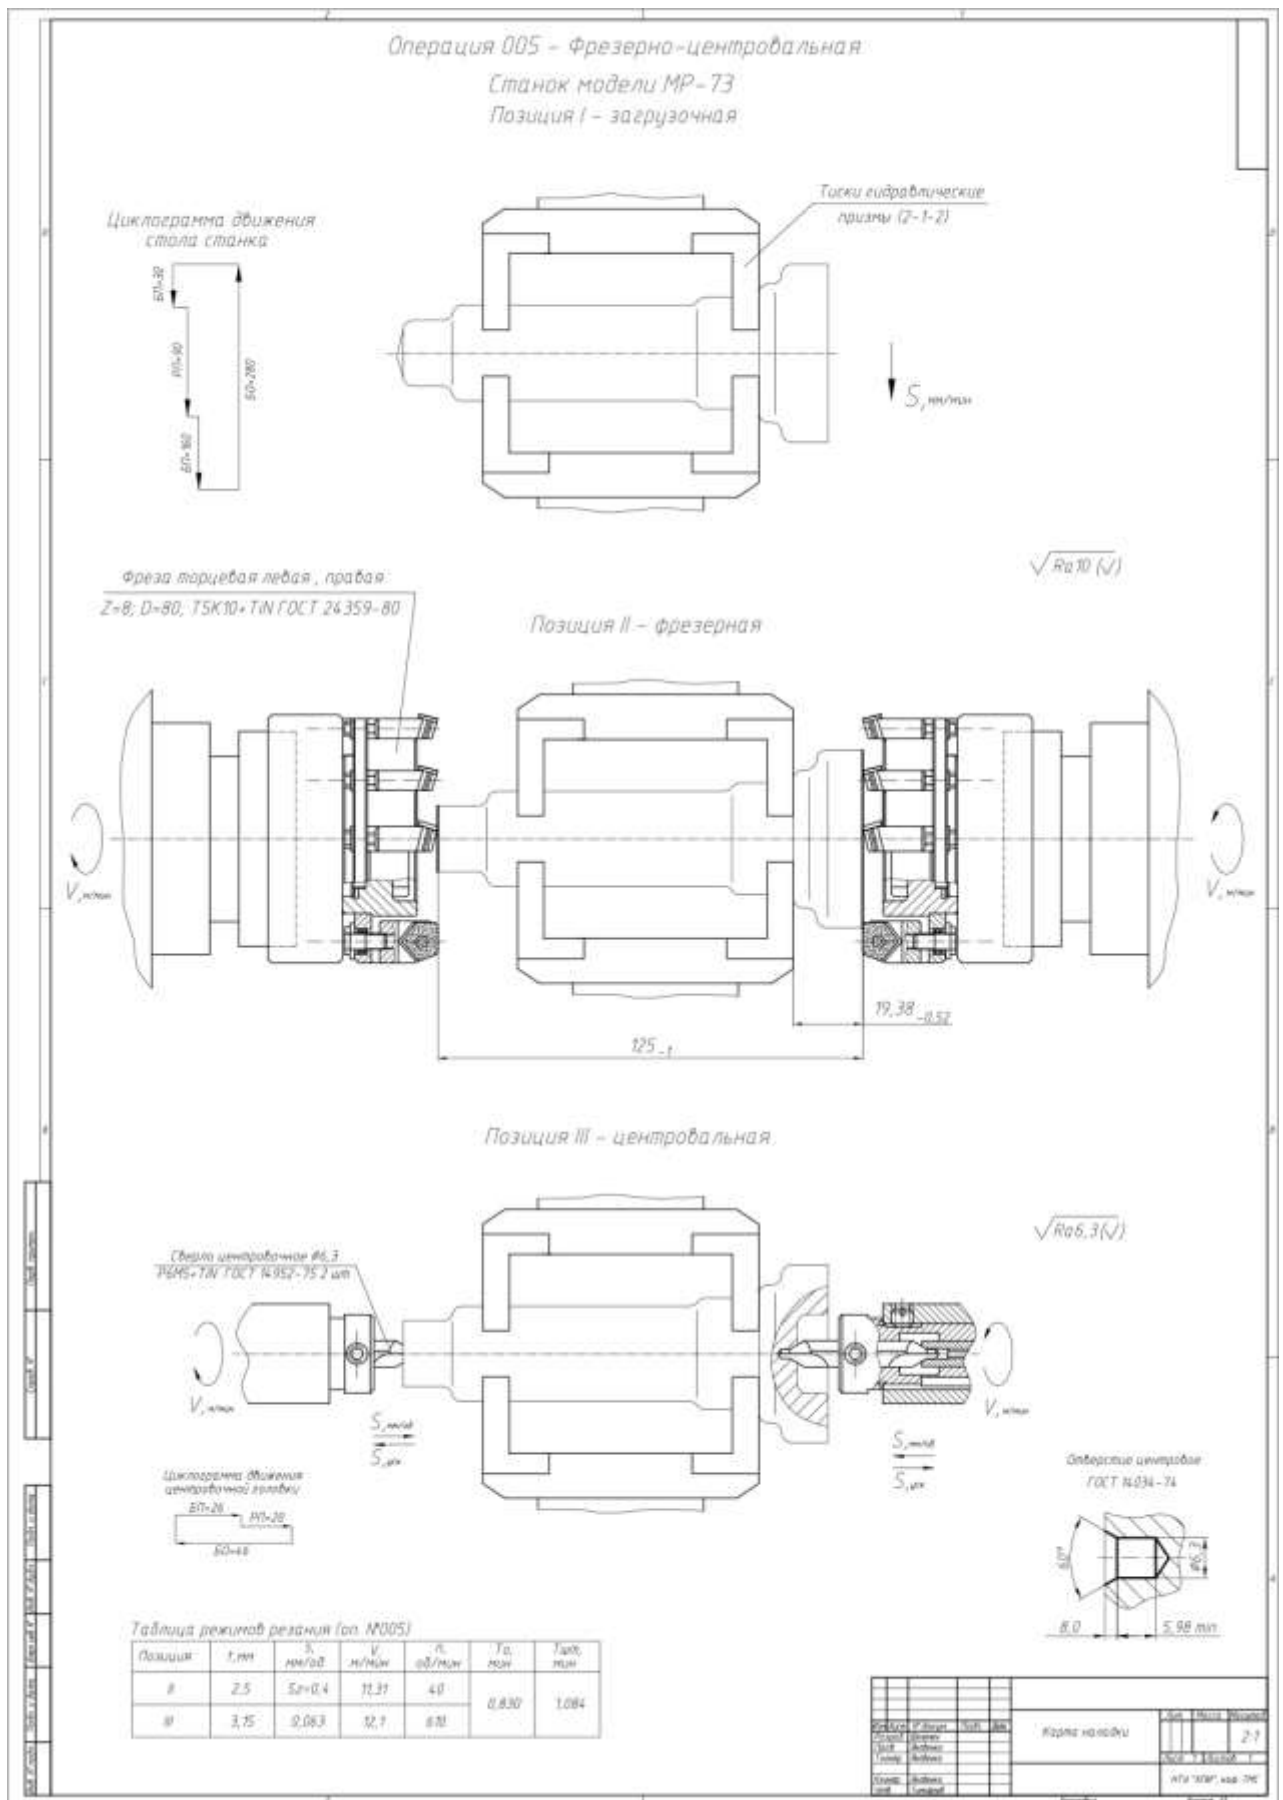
Приклад оформлення інструментального налагодження на фрезерно-центрувальну операцію.
